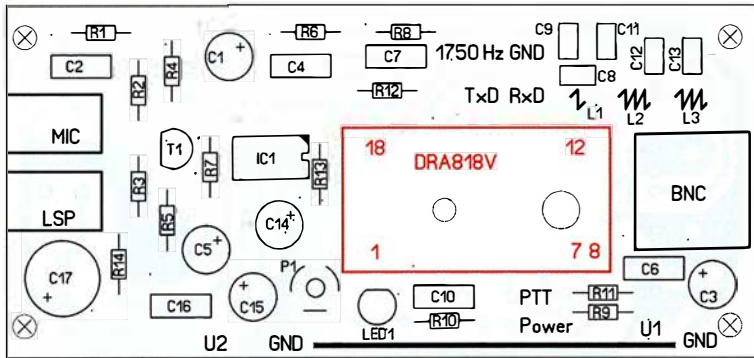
Bestückungsplan der 2-m-HF-Baugruppe, M 1:1; das VHF-Transceivermodul befindet sich auf der Unterseite der Platine.
